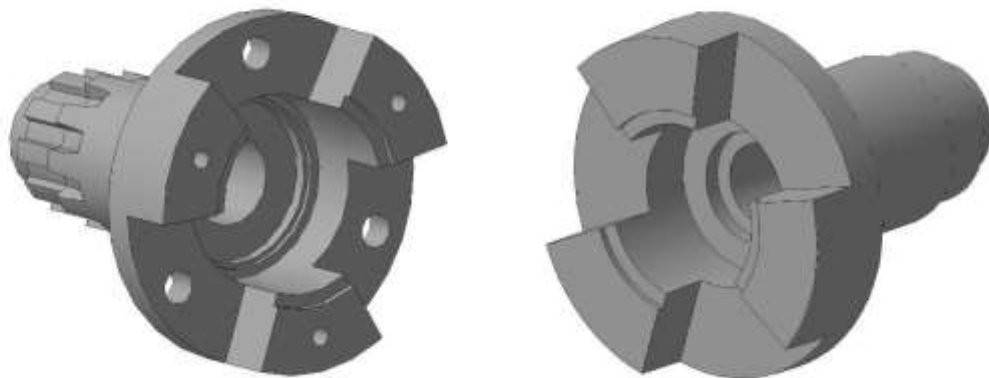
Тривимірні моделі деталі та заготовки
